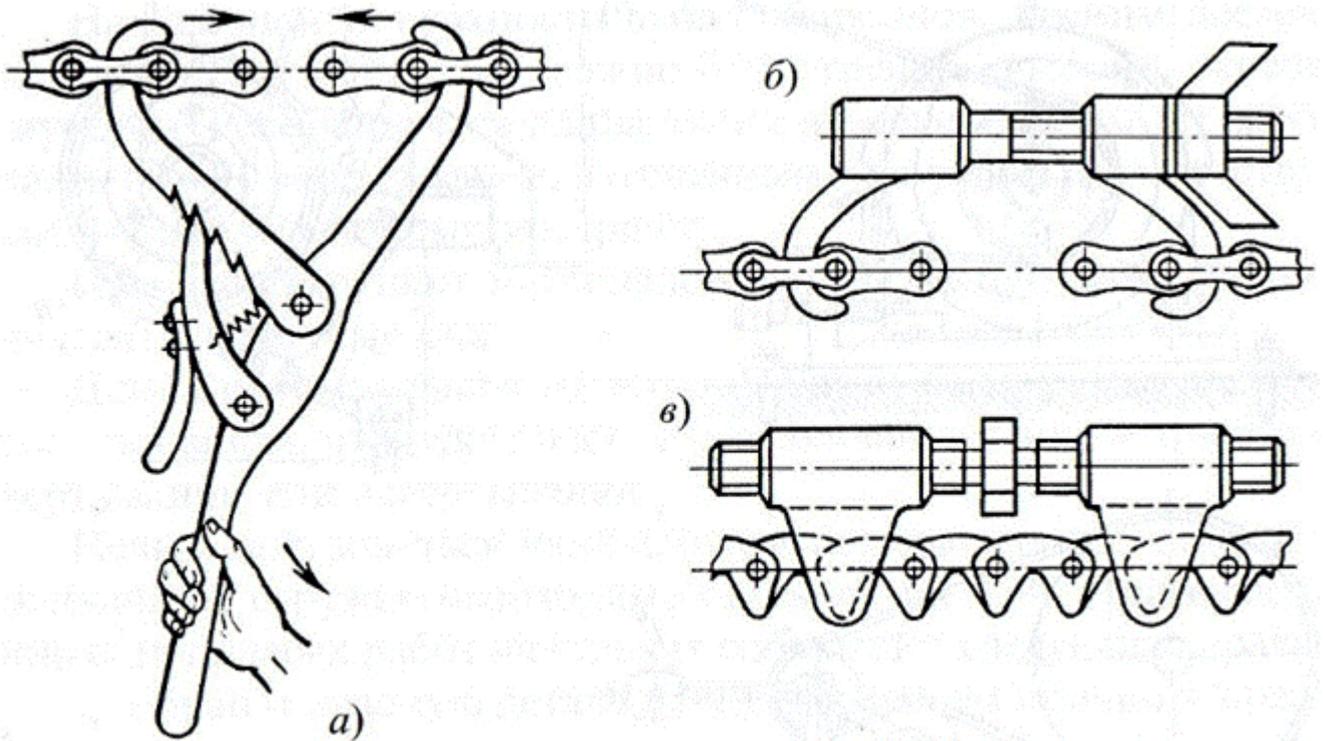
Стяжки для соединения концов цепей: а — рычажная; б — винтовая для роликовой и втулочной цепей; в — винтовая для зубчатой цепи
